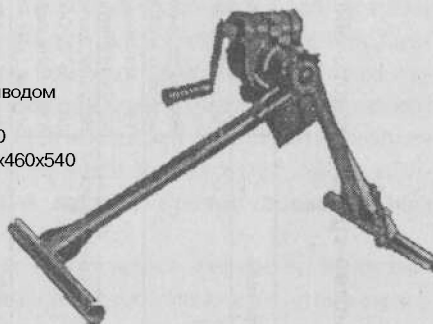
Приспособление для снятия и установки ГМП автобусов ЛиАЗ-677, мод. П-235М
